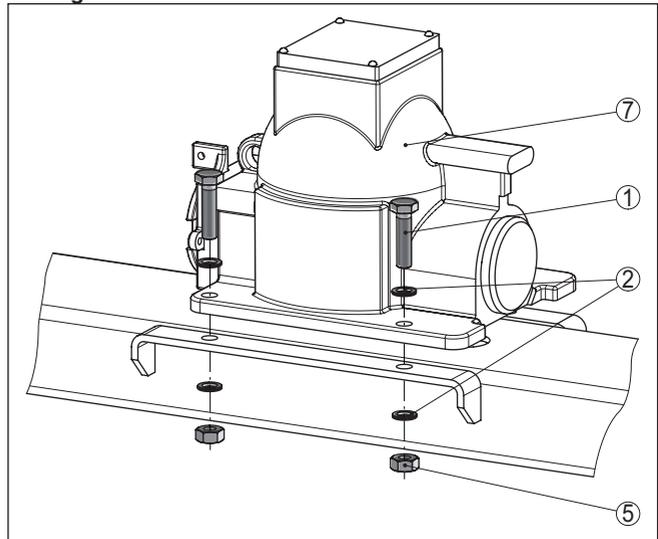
Montage des Strahlenschutzbehälters auf dem Messrahmen
